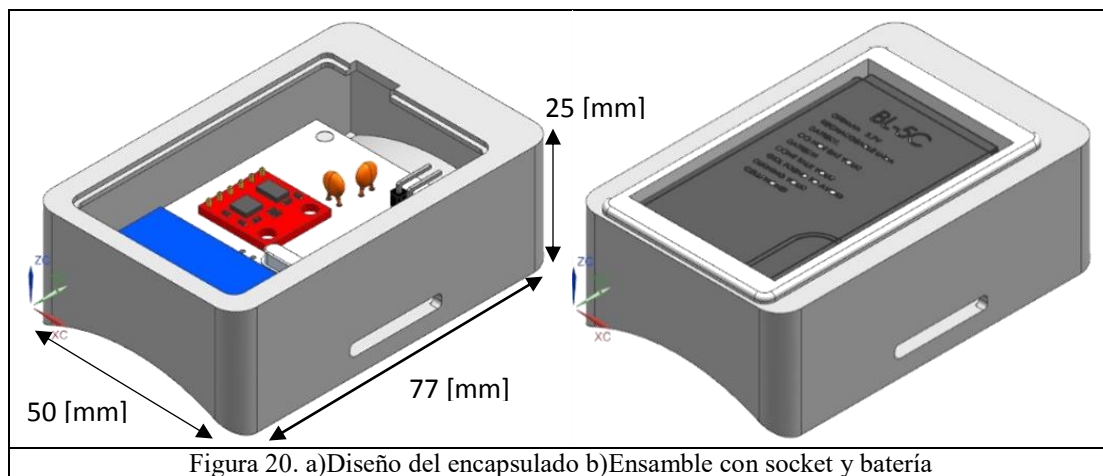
a)Diseño del encapsulado b)Ensamble con socket y batería
